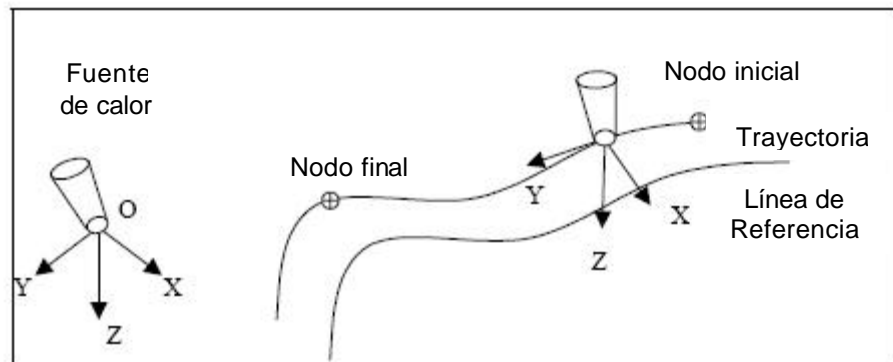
Ilustración de los grupos necesarios para definir la trayectoria de la soldadura (ESI Group, Process, 2009).
